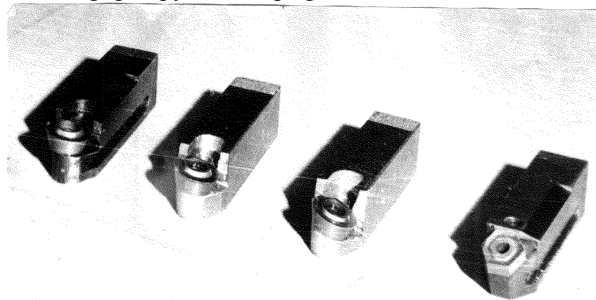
Резцы с механическим креплением пластин из твердого сплава для обработки внутреннего кольца подшипника
